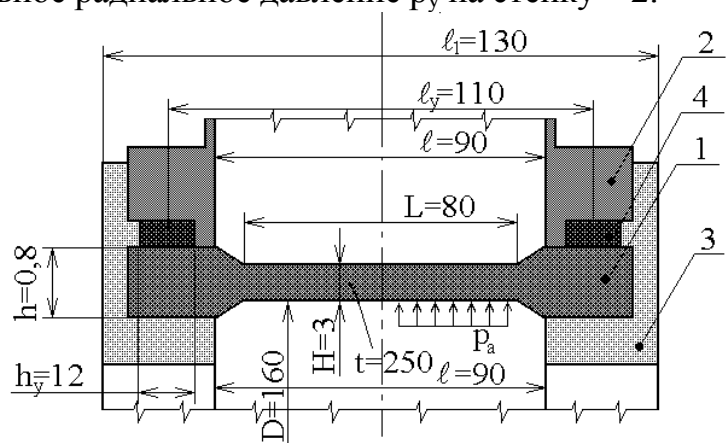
Схема трубчатой стенки вакуумной камеры: 1 – стенка из УУКМ; 2 – опорный фланец вакуумной камеры (металл); 3 – торцовый опорный кольцевой фланец (металл); 4 – уплотнитель на вакуум (резина).
